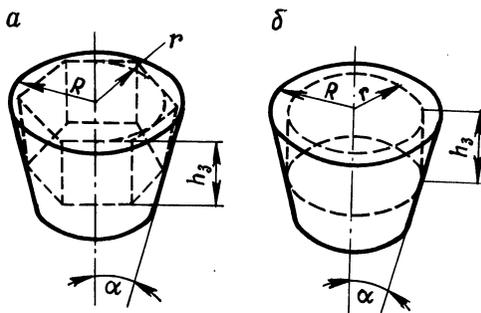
Изменение формы режущей пластинки вследствие ее изнашивания: a — при периодическом повороте пластинки; b — при непрерывном повороте пластинки
